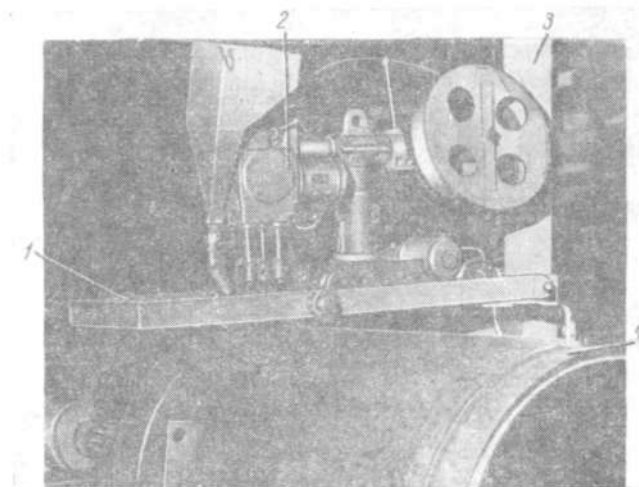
Установка для сварки кольцевых наружных швов.
